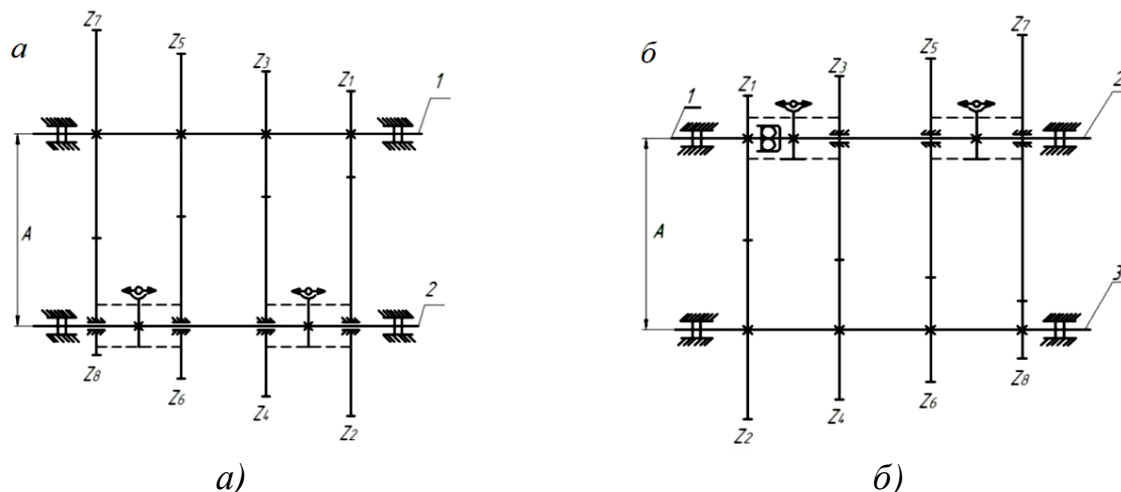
Принципиальная кинематическая схема 4-х ступенчатой коробки передач:
